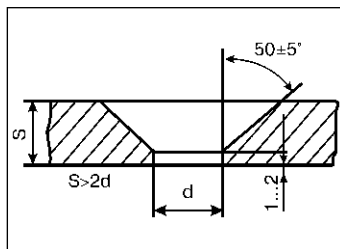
Схема подготовки отверстия под заварку раззенкованием
